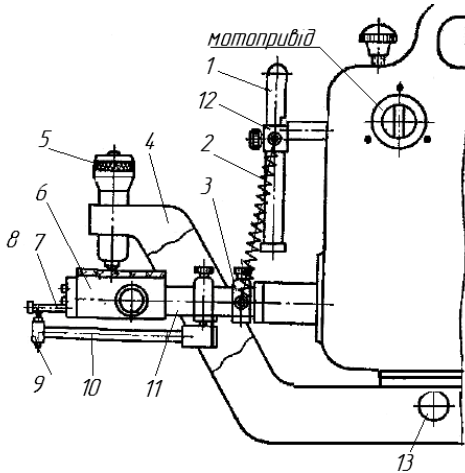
Пристосування для перевірки хвилястості поверхні.
